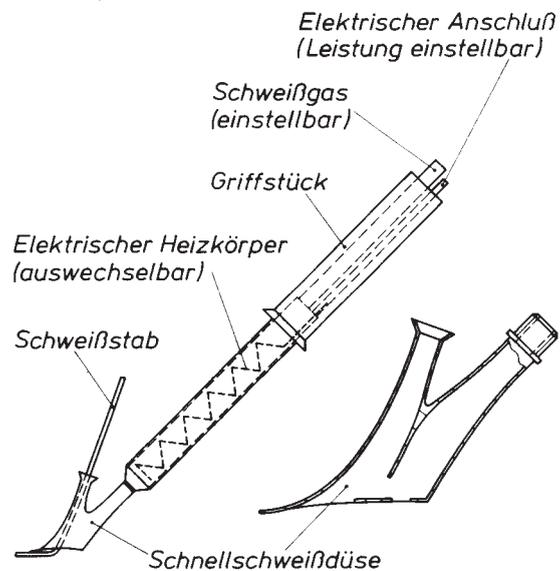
Warmgasschweißgerät mit Schnellschweißdüse (schematisch)
